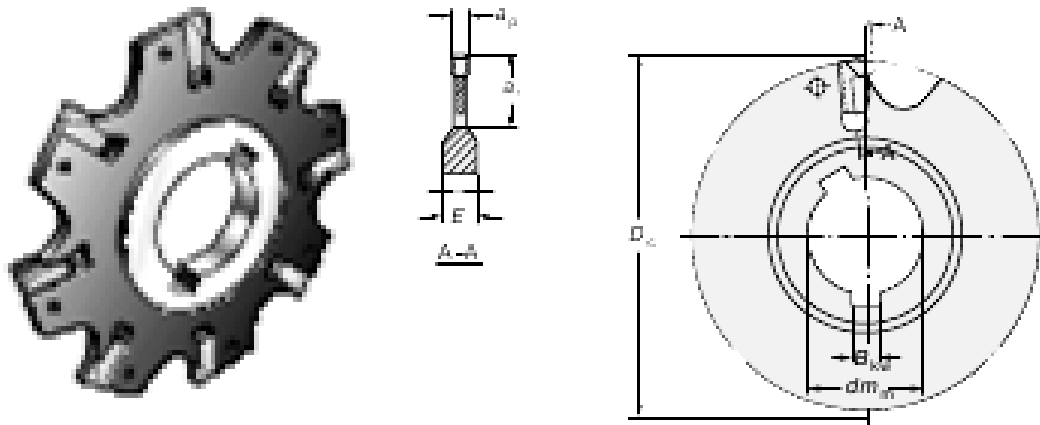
Конструкция прорезной фрезы Шведской фирмы Sandvik Coromant с механическим креплением режущих пластин специальной формы
